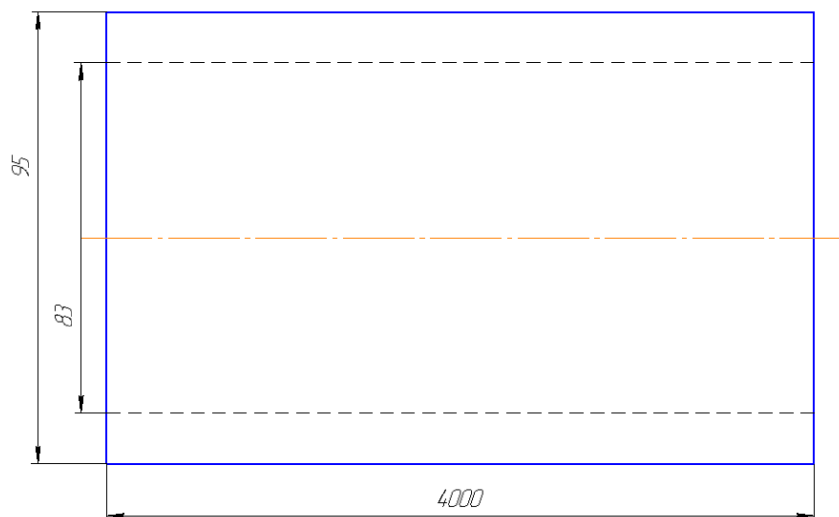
Ескіз заготовки з гарячекатаного прокату
